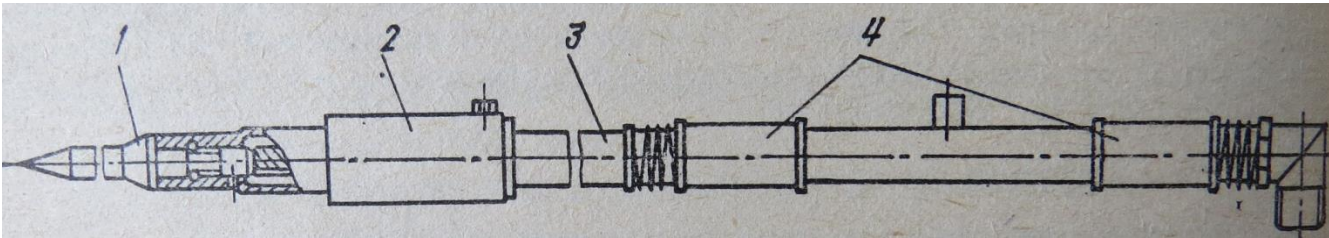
Принципова схема пристрою ОК-3 для прибирання заколів:
